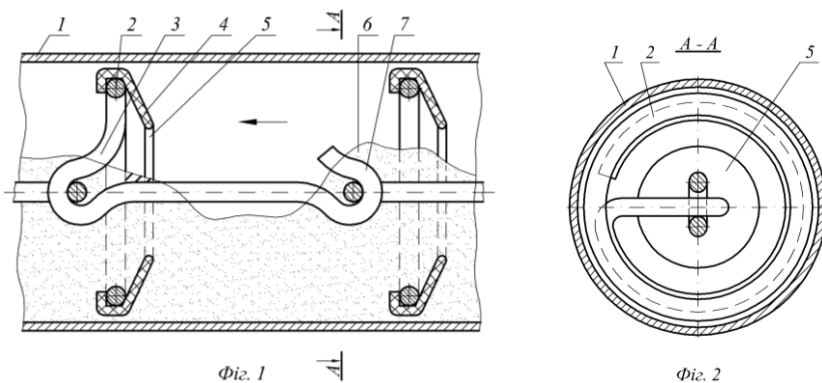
Робочий орган шайбового скребкового транспортера-змішувача
